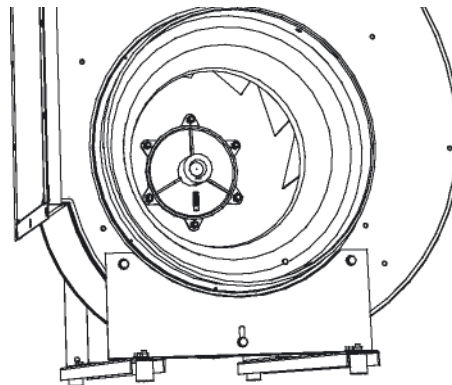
GTLB-1 -022...071 Retire la fijación de la campana y la rueda del árbol motor.
